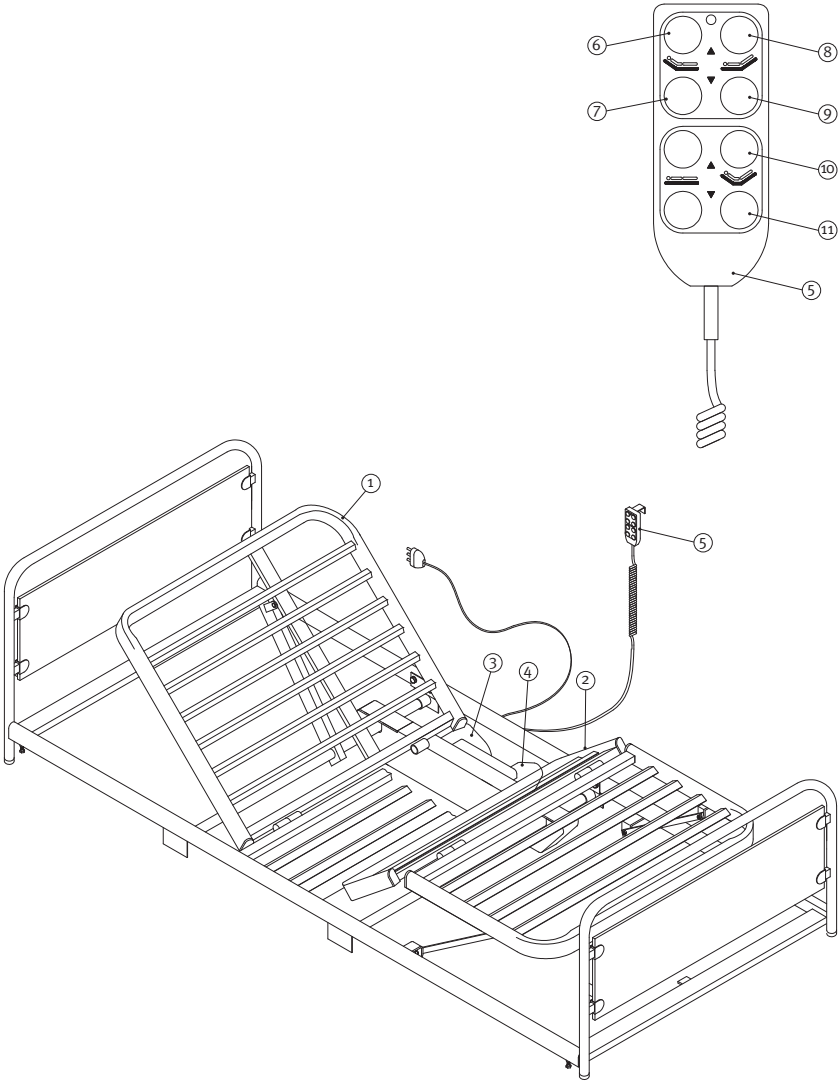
Regolazione della sezione testa e della sezione gambe del letto Art. A 7034/AE.
